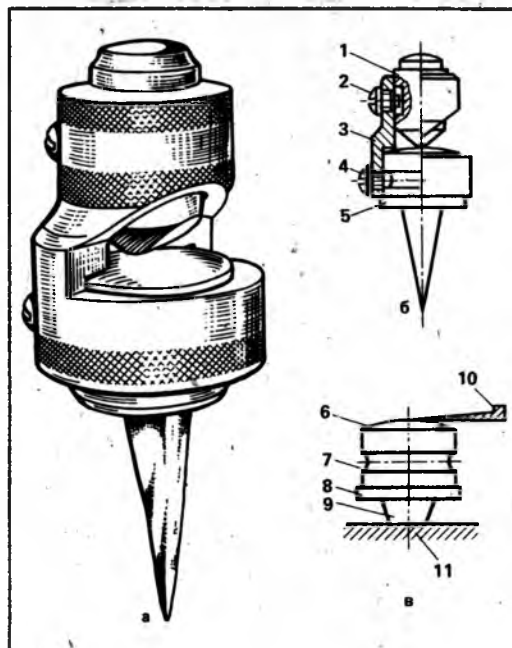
Косоотбой КС-1: 1 — боек; 2, 4 — винты; 3 — корпус; 5 — бабка; 6 — рабочая поверхность бабки; 7 — проточка; 8 — бурт; 9 — хвостовик; 10 — нож косы; 11 — опора
